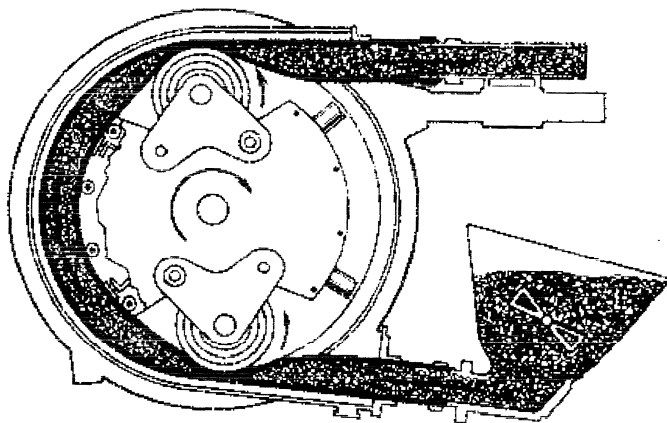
Качающий узел роторно-шлангового бетононасоса
